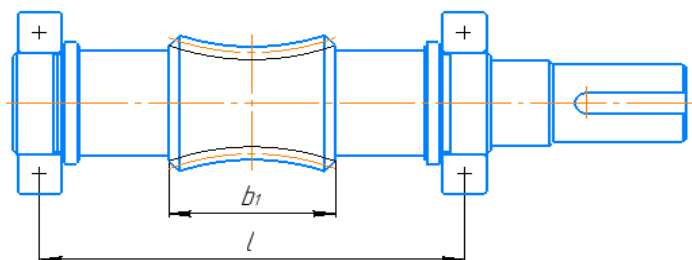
Конструктивні елементи глобоїдного черв'яка
